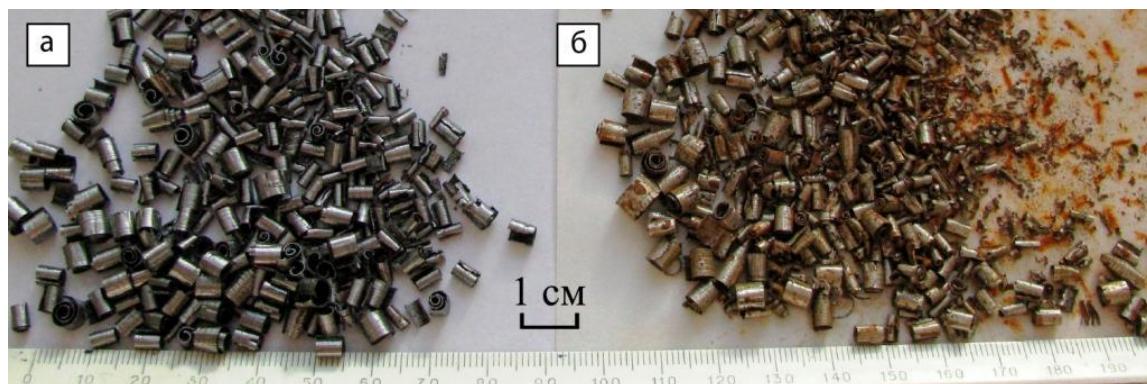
Вигляд стружки, що утворилась під час механічної обробки: а – із ЗОР, б – з водою
